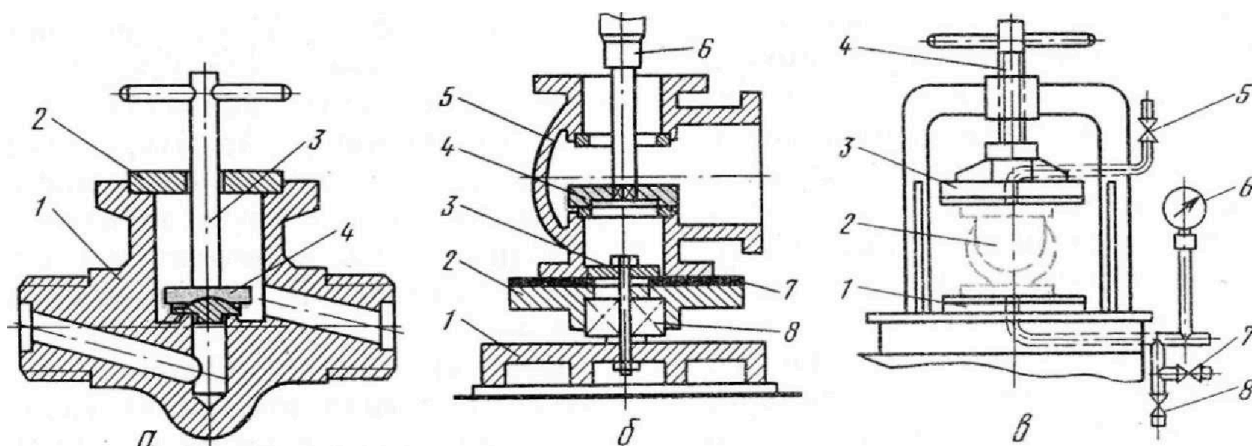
Приспособления для притирки уплотнительных поверхностей седел
